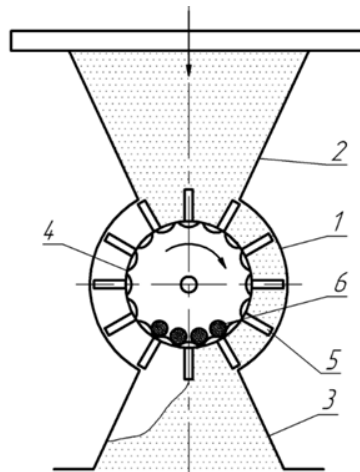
Схема роторного живильника з очищенням ротора: 1 – циліндричний корпус; 2 – завантажувальна лійка; 3 – розвантажувальна лійка; 4 – вал, що обертається; 5 – лопаті; 6 – важкі кулі
